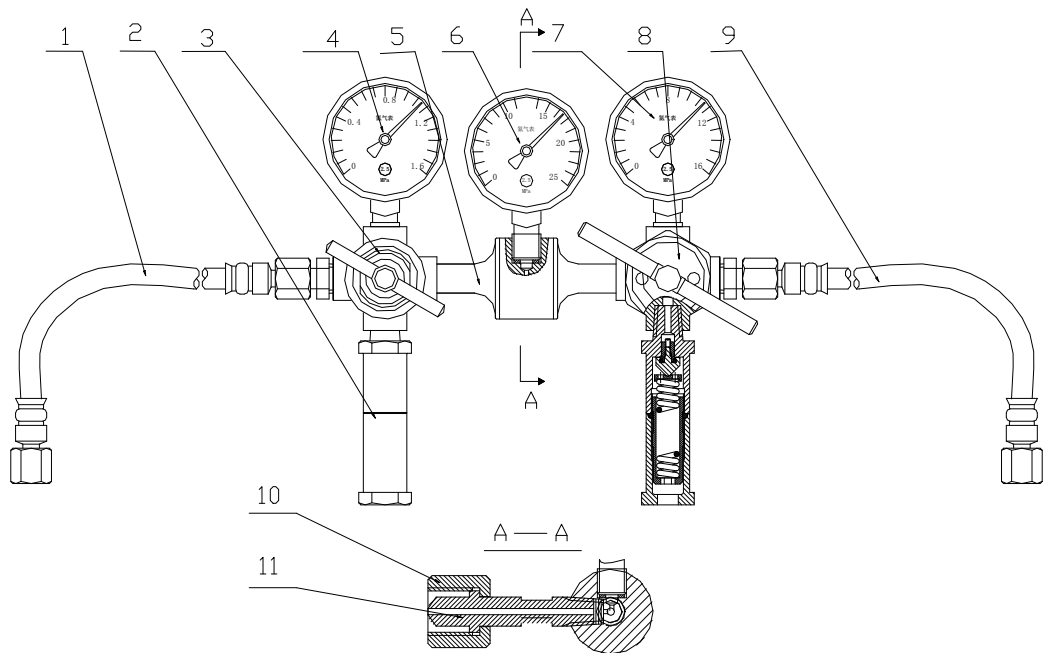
保险阀组件结构图 The structure diagram of the safety valve assembly
